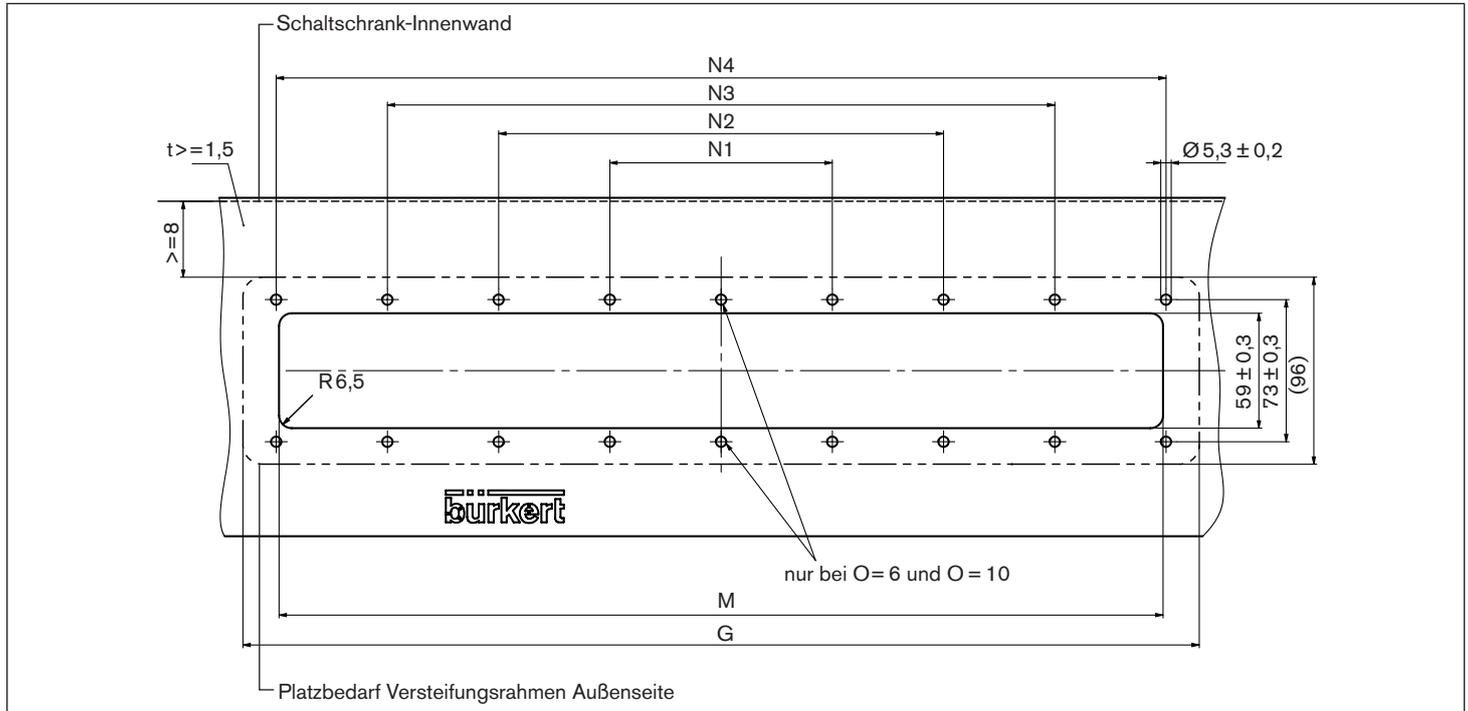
Flanschbilder AirLINE Quick – Maße siehe Tab. 1 auf Seite 26
